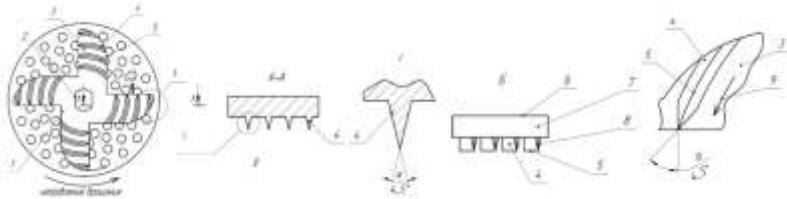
Конструкция крестообразного ножа с лопастями, на задних поверхностях которых имеются режущие лезвия (1 – ступица ножа; 2 – посадочное отверстие; 3 – лопасть ножа; 4 – режущее лезвие; 5 – режущая кромка; 6 – режущая кромка на поверхности лопасти; 7 – передняя поверхность лопасти; 8 – режущая кромка на фронтальной поверхности лезвия, расположенного на спинке лопасти; 9 – направление вращения лопасти)
